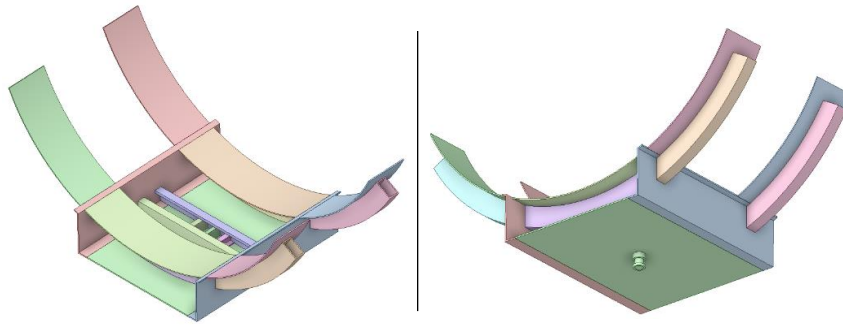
Vistas isométricas del Tornamesa ensamblado
